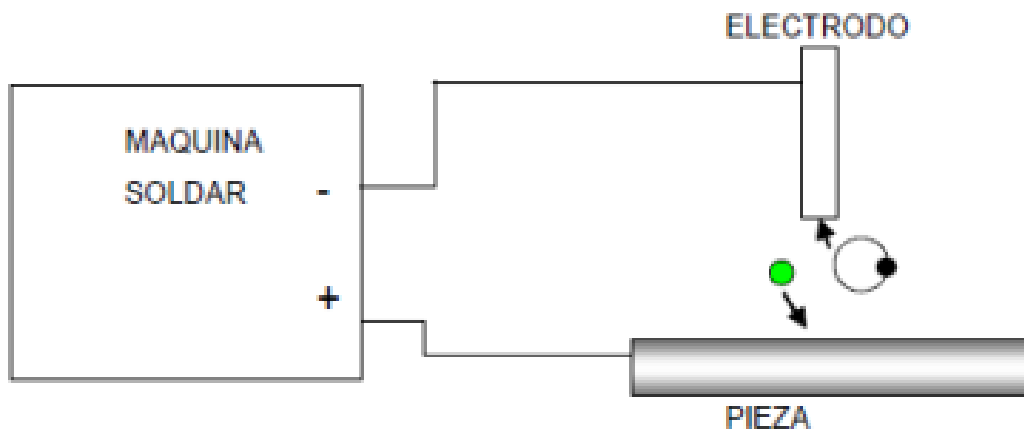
Esquema de Polaridad Directa de la Soldadora GMAW.
